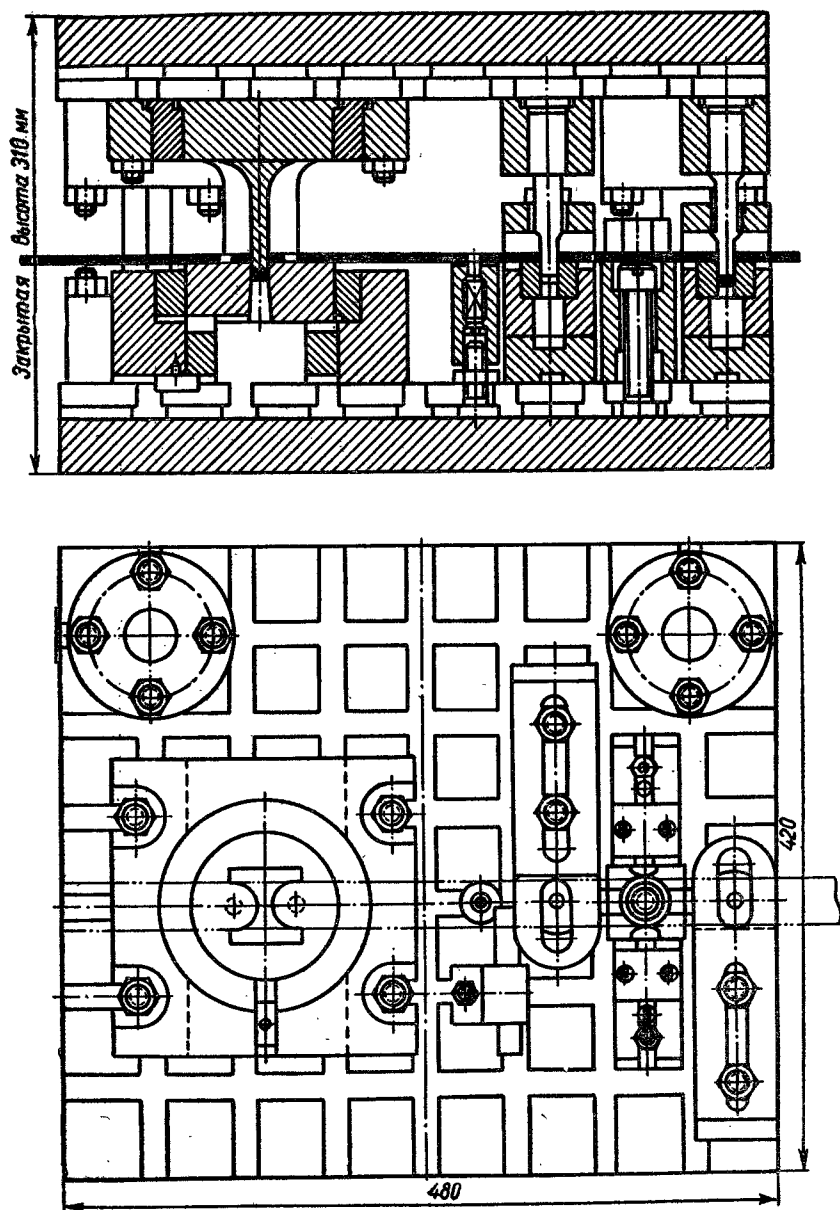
Универсально-сборный штамп для пробивки и фигурной отрезки детали
